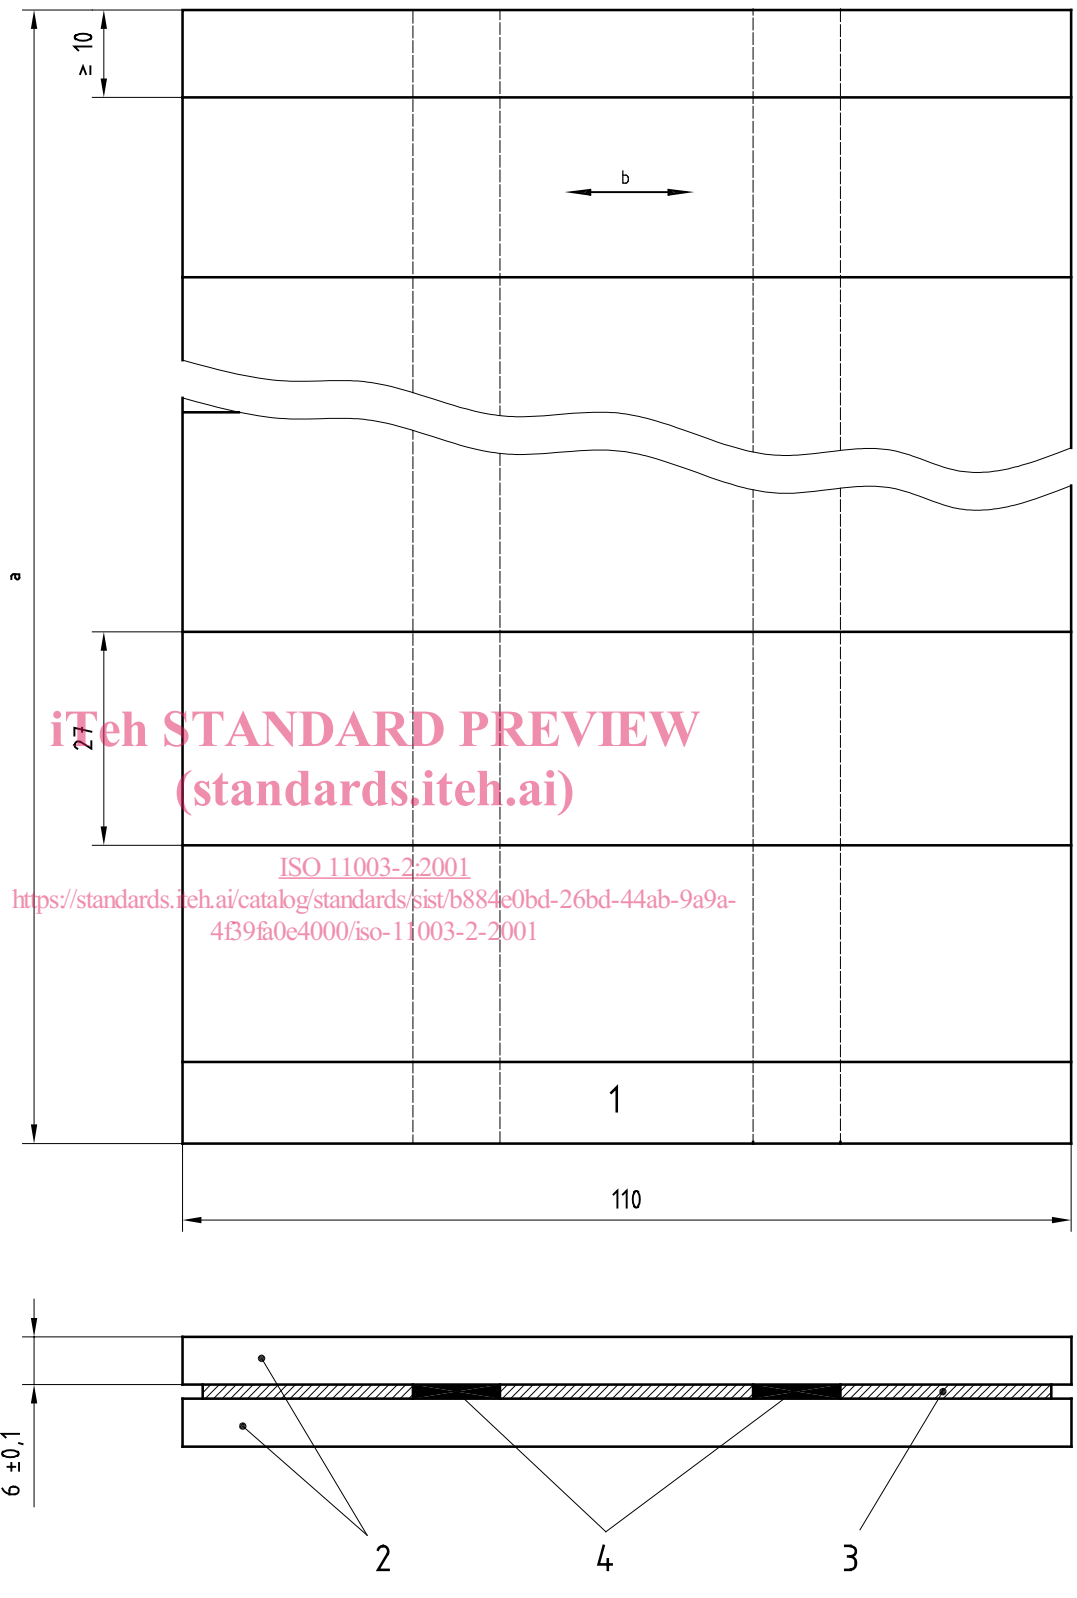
Panneau non coupé pour fabriquer les assemblages d'éprouvettes
